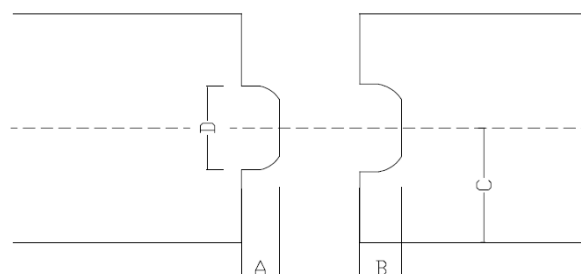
Dimensions du parachèvement des bords rainure et languette
